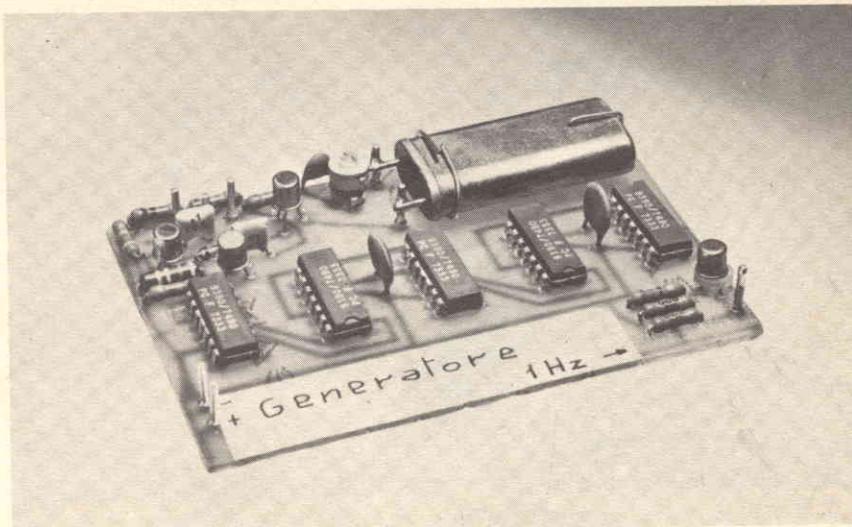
Circuito stampato di figura 9 a montaggio ultimato.
